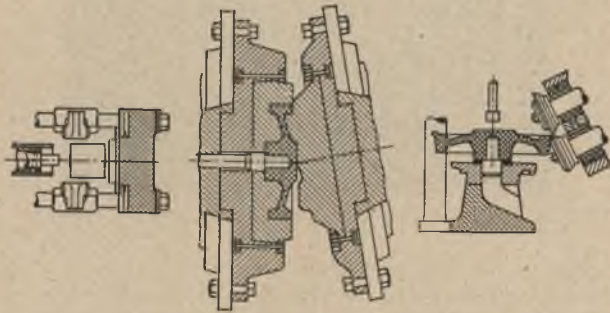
Radscheiben-Walzwerk: Walzvorgang nach E. Slick.
